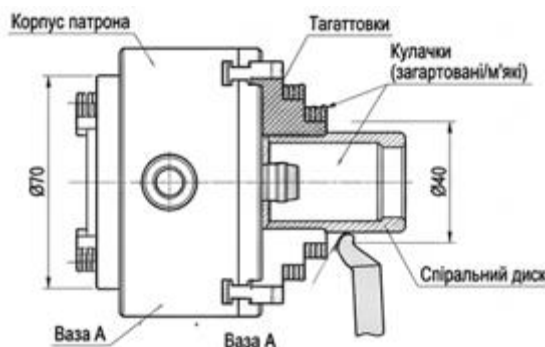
3-кулачковий патрон ЧПК верстата
